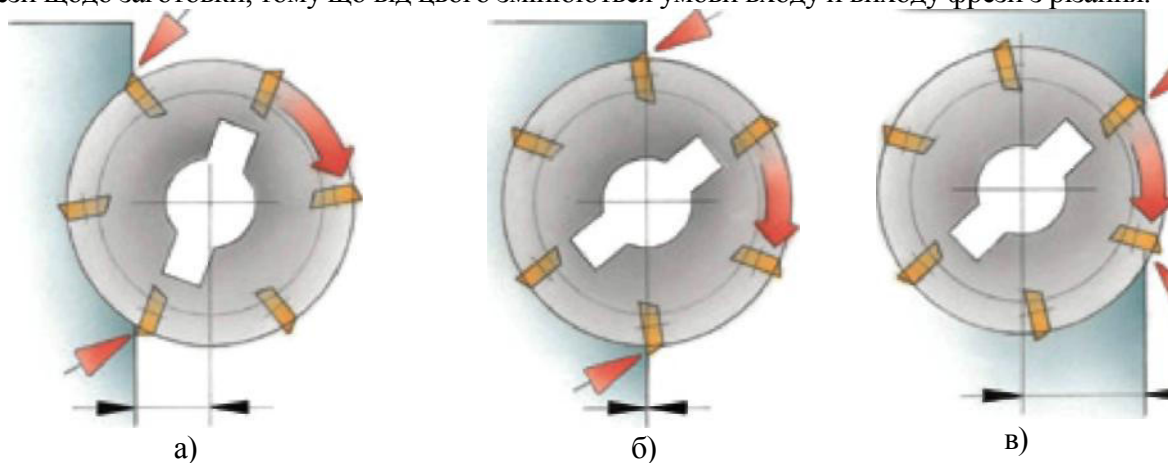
Умови входу й виходу з різання при різному розташуванні торцевої фрези
